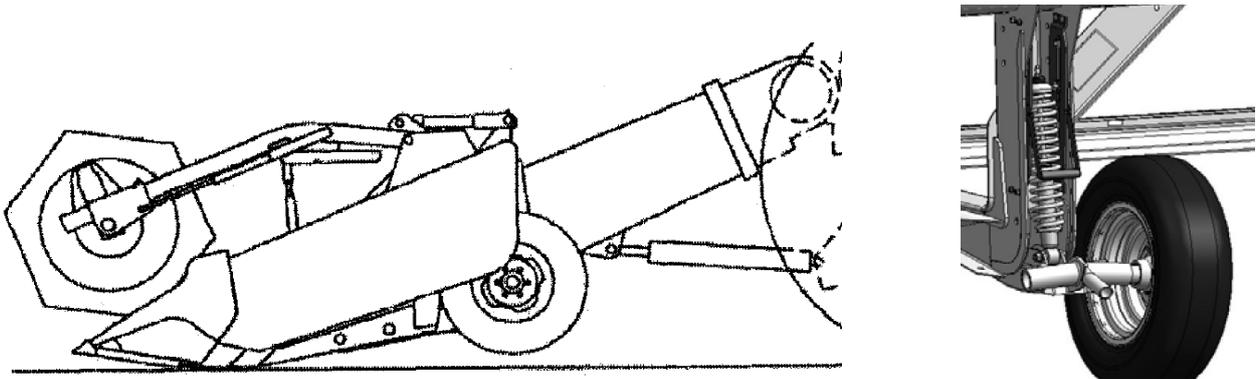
Las ruedas estabilizadoras se pliegan cuando el cabezal trabaja flotante y se bajan cuando el cabezal trabaja elevado para estabilizarlo.
